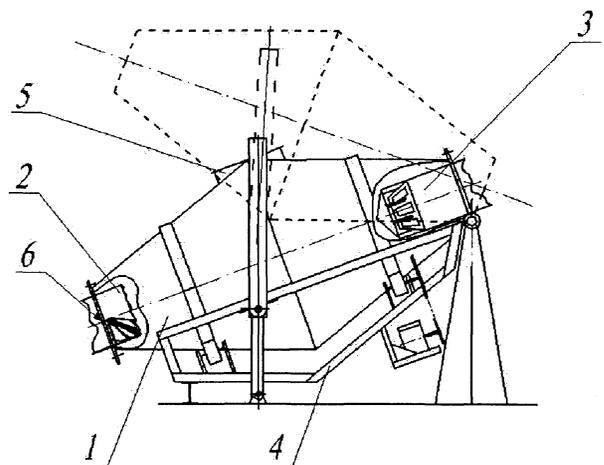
Качающееся сушило: 1 – корпус; 2 – завихритель; 3 – сепаратор; 4 – подвижная качающаяся рама; 5 – загрузочное окно; 6 – разъемное соединение; 7 – привод (пат. РБ № 2428):
